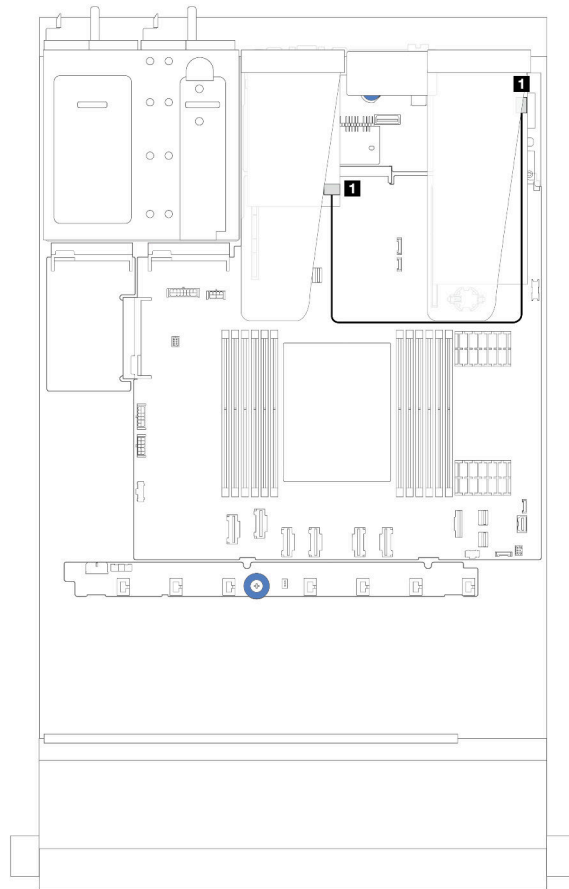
Disposición de los cables del módulo de alimentación flash RAID en el conjunto de expansión
